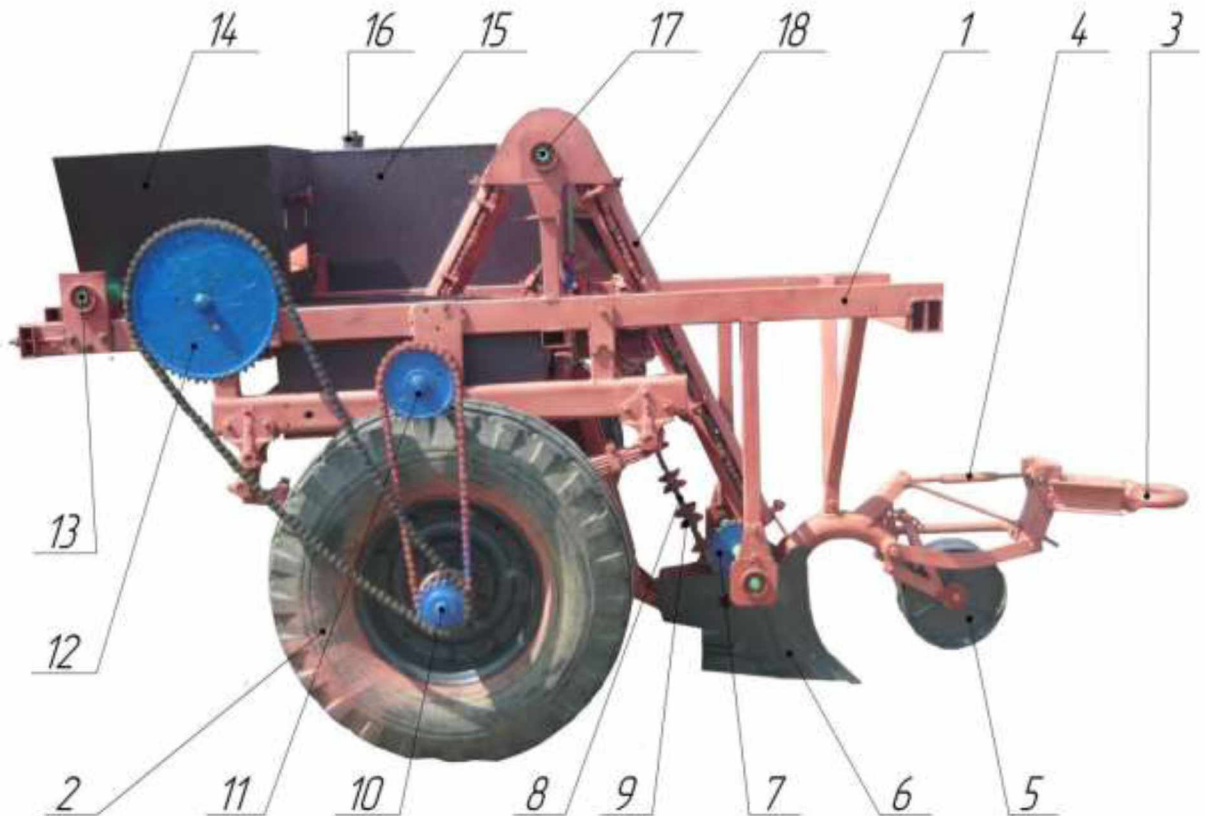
Експериментальна картоплесадильна машина: 1 - рама; 2 - колесо опорно-приводне; 3 - причіпна сниця; 4 - регулювальна тяга; 5 - колесо опорно-копіювальне; 6 - сошник-борозноутворювач; 7 - ведена зірочка; 8 - елеваторний транспортер; 9 - ложечка; 10 - зірочка приводна подвійна; 11 - ведена зірочка елеваторного транспортера; 12 - ведена зірочка донного транспортера бункера насінневих бульб; 13 - ведений вал донного транспортера; 14 - бункер насінневих бульб; 15 - резервуар робочого розчину; 16 - заливна горловина резервуара робочого розчину; 17 - вал обвідний зірочки елеваторного транспортера; 18 – кожух
